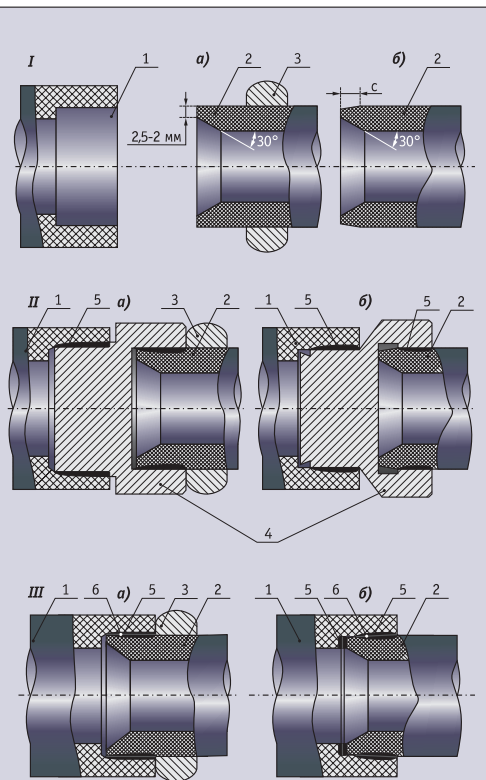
Схема раструбной (а) и раструбно-стыковой (б) сварки нагретым инструментом: I — подготовка к сварке; II — оплавление деталей на инструменте; III — сварное соединение 1 — раструб; 2 — труба; 3 — ограничительный хомут; 4 — нагревательный инструмент; 5 — оплавленная зона детали; 6 — сварной шов
